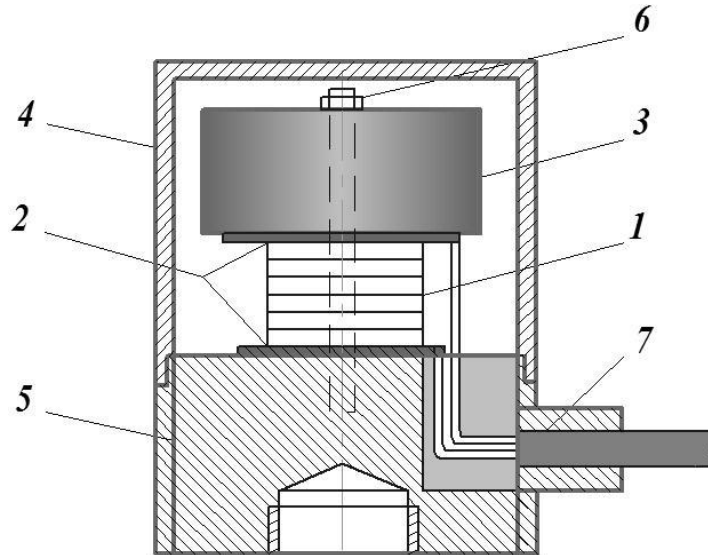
Конструкція ПГ: 1 – ПЕ; 2 – ізолятори; 3 – ІМ; 4 – основа; 5 – герметичний корпус; 6 – гвинт; 7 – вивідний кабель
